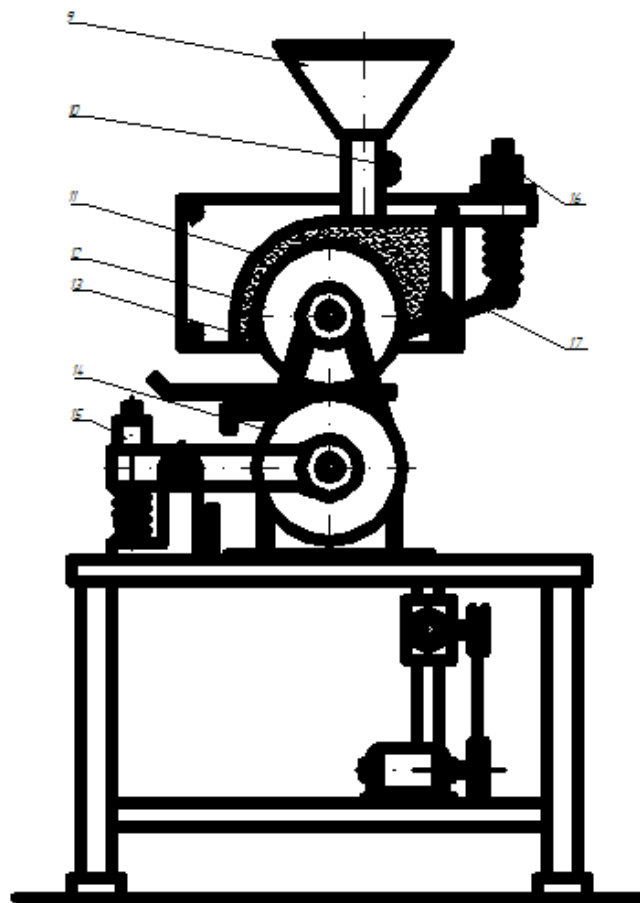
Пристрій для нанесення клею по контуру взуттєвої деталі
